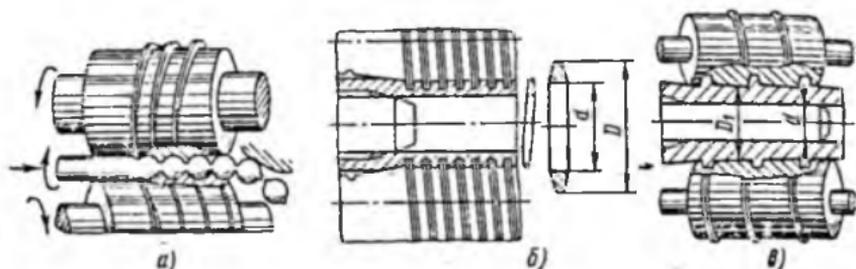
Схемы поперечно-винтовой прокатки заготовок; а — шаровых; б — кольцевых; в — ребреных труб
